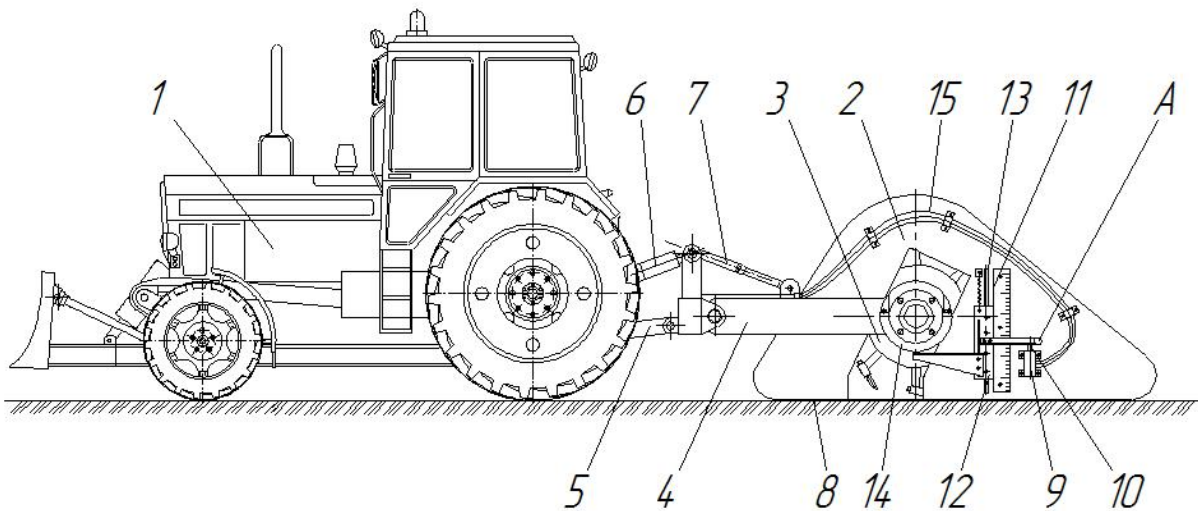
Загальний вигляд машини для руйнування дорожніх покриттів: 1 – базовий трактор; 2 - плаваючий кожух; 3 – дорожня фреза; 4 – балки; 5 – тяги; 6, 7 – гідроциліндри керування; 8 – лїжа; 9 - золотник; 10 – шток; 11, 12 – відповідно основна та кінцева частина важеля; 13 – стійка вертикальна; 14 – опора; 15 – трубопровід.
